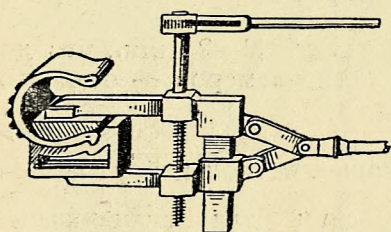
Аппарат для вулканизации боковин и бортов покрывки
